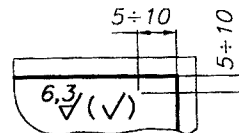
Представление шероховатости необозначенных на чертеже поверхностей
